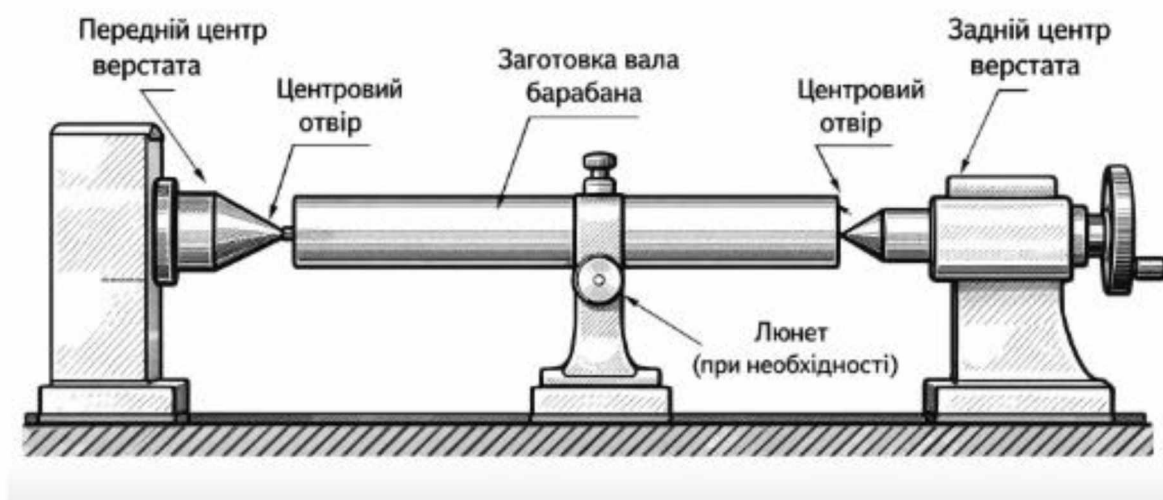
Схема базування заготовки вала барабана в центрах
